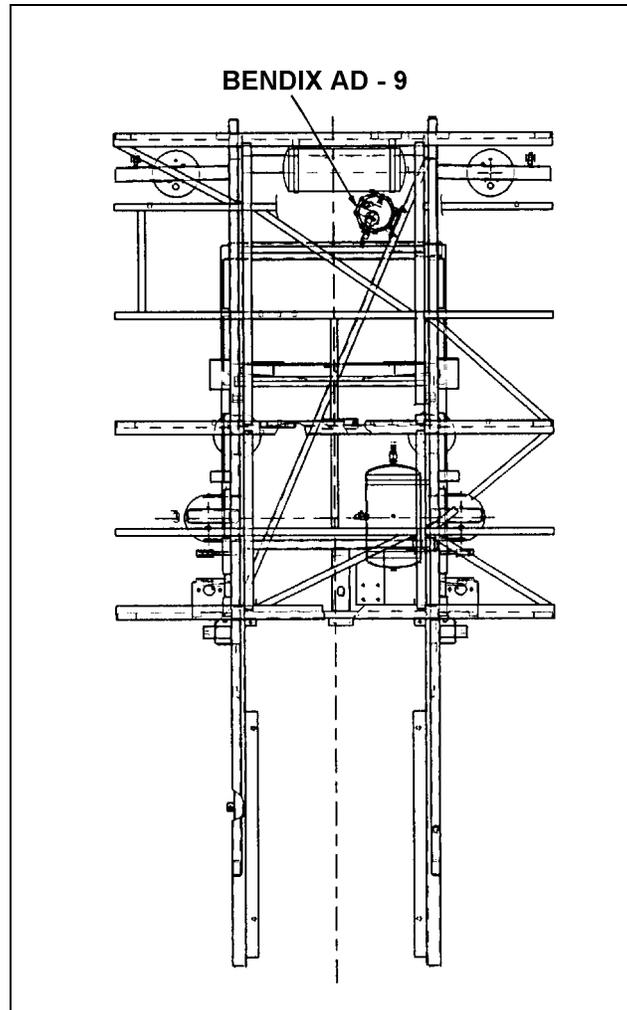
SOUS-CHÂSSIS ARRIÈRE
